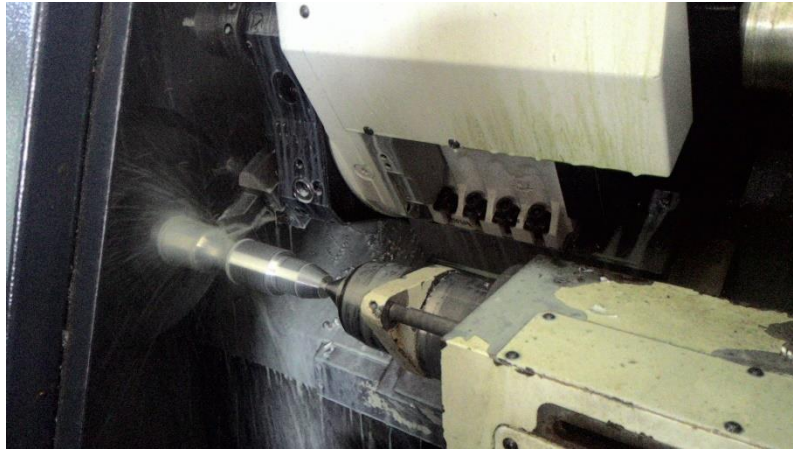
Ham malzemenin universal tornada işlenmesi.
